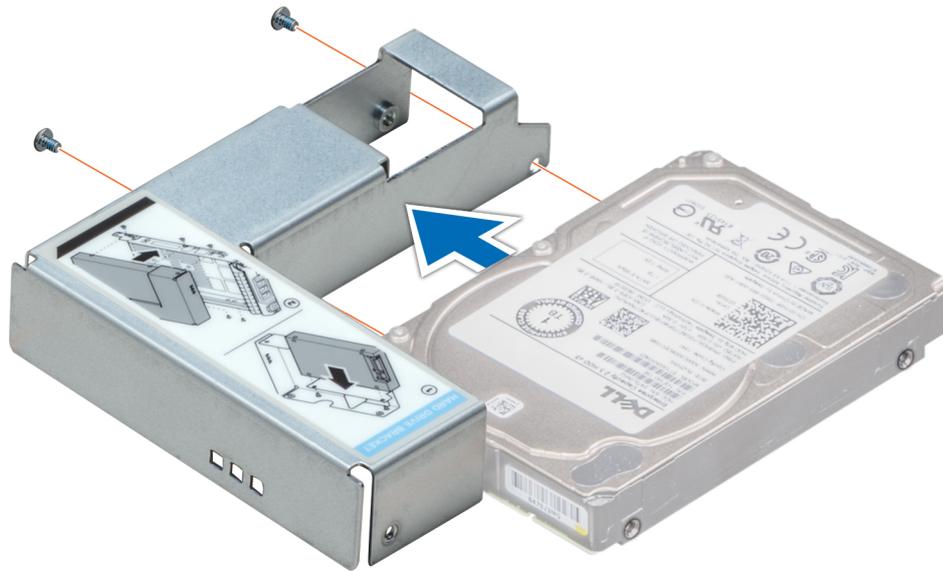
Installieren eines 2,5-Zoll-Laufwerks in einem 3,5-Zoll-Laufwerkadapter
